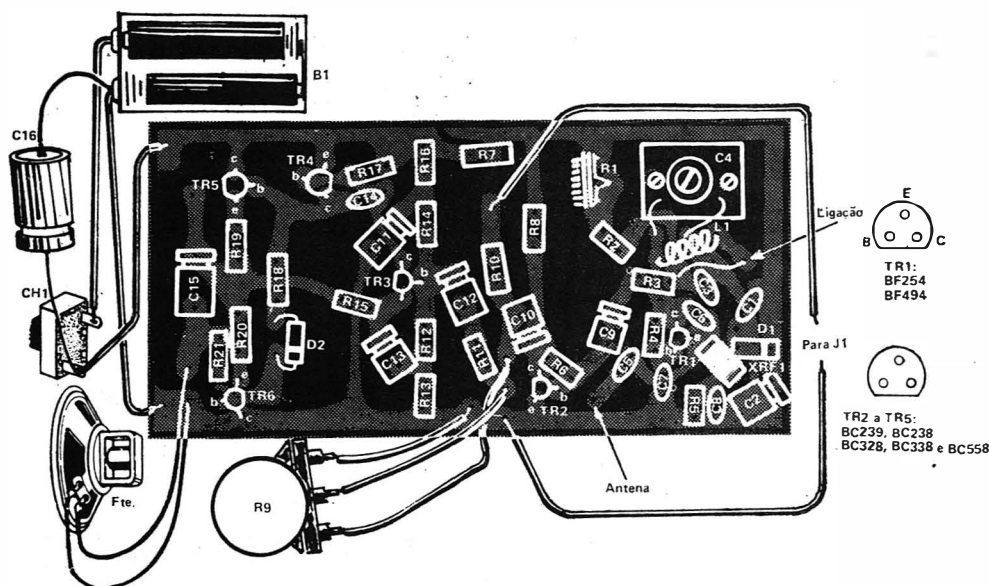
Disposição dos componentes sobre a plaqueta da Fig. 2.
